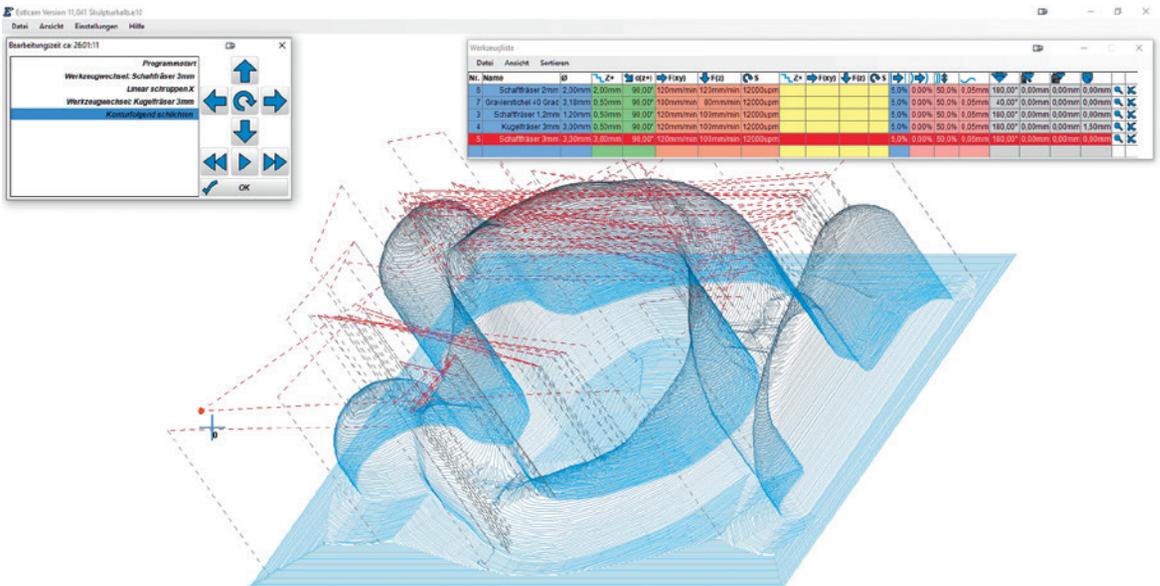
Das konturparallele Schichten folgt der Oberfläche, die so besonders glatt wird.
